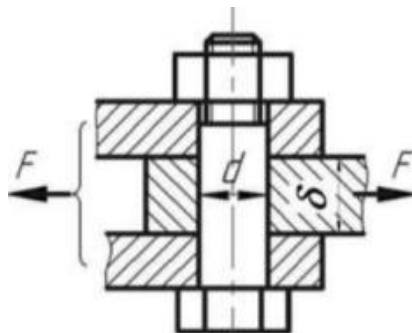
Схема з'єднання болтом, встановленим у отвори деталей без зазору
